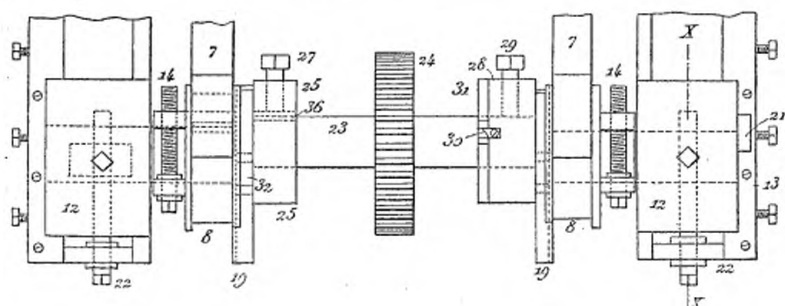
Plan de la forme du porte-outil appliqué au système Gœhring.
